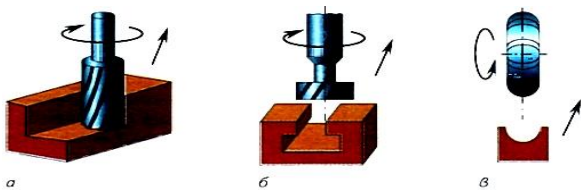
Виды фрез: а, б — концевые; в — фасонная
